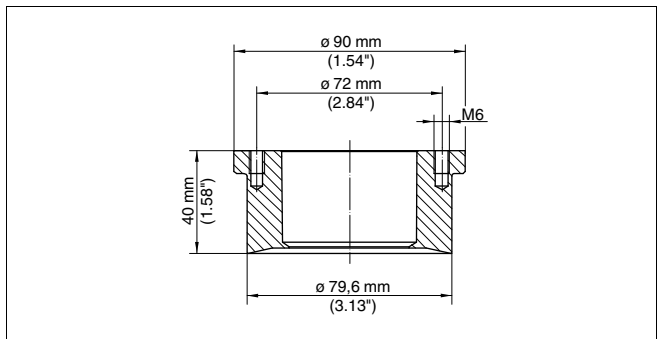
Maße Einschweißstutzen LB für Spannflansch
